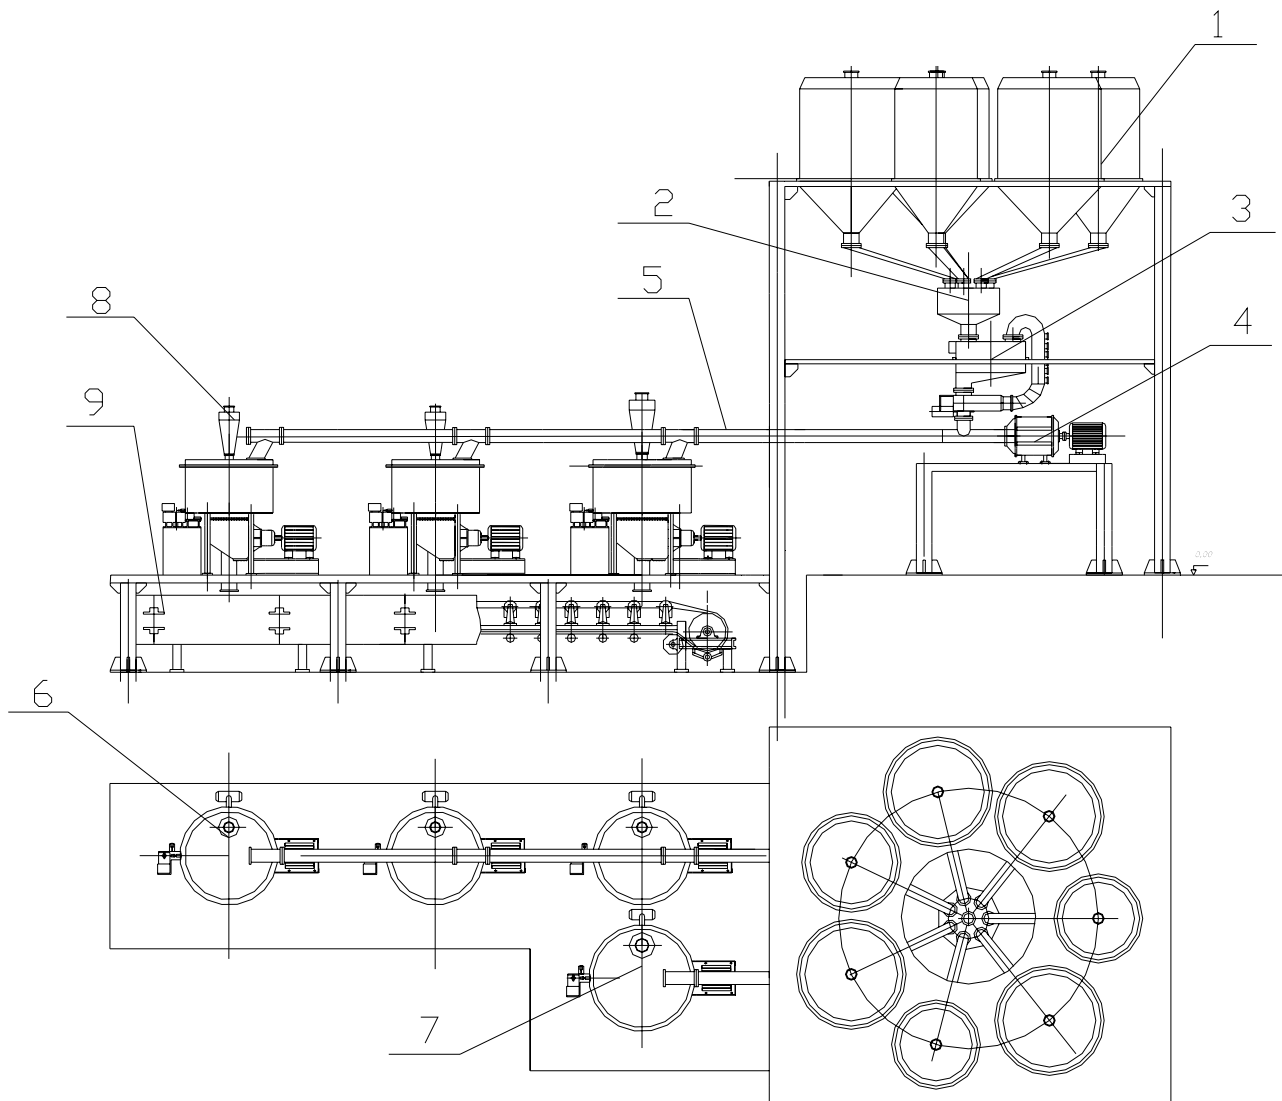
Схема комплекса для приготовления песчано-глинистой смеси с различными типами смесителей и камерой предварительного перемешивания:
